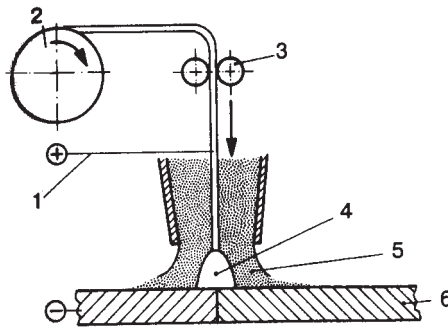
Схема процесу зварювання у середовищі захисного газу:
